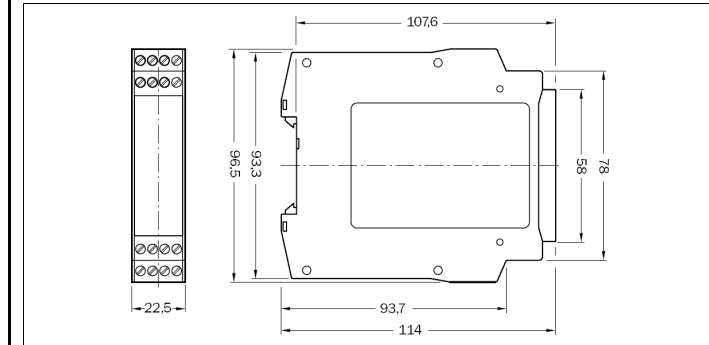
Maßbild UE11-4DX mit Steckblockklemmen (mm)
